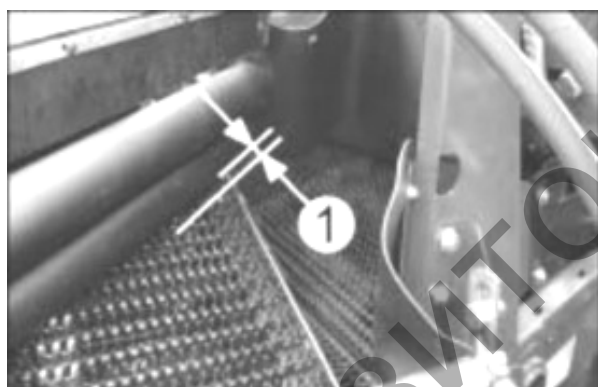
Регулировка зазора сдвоенного счищающего вальца
